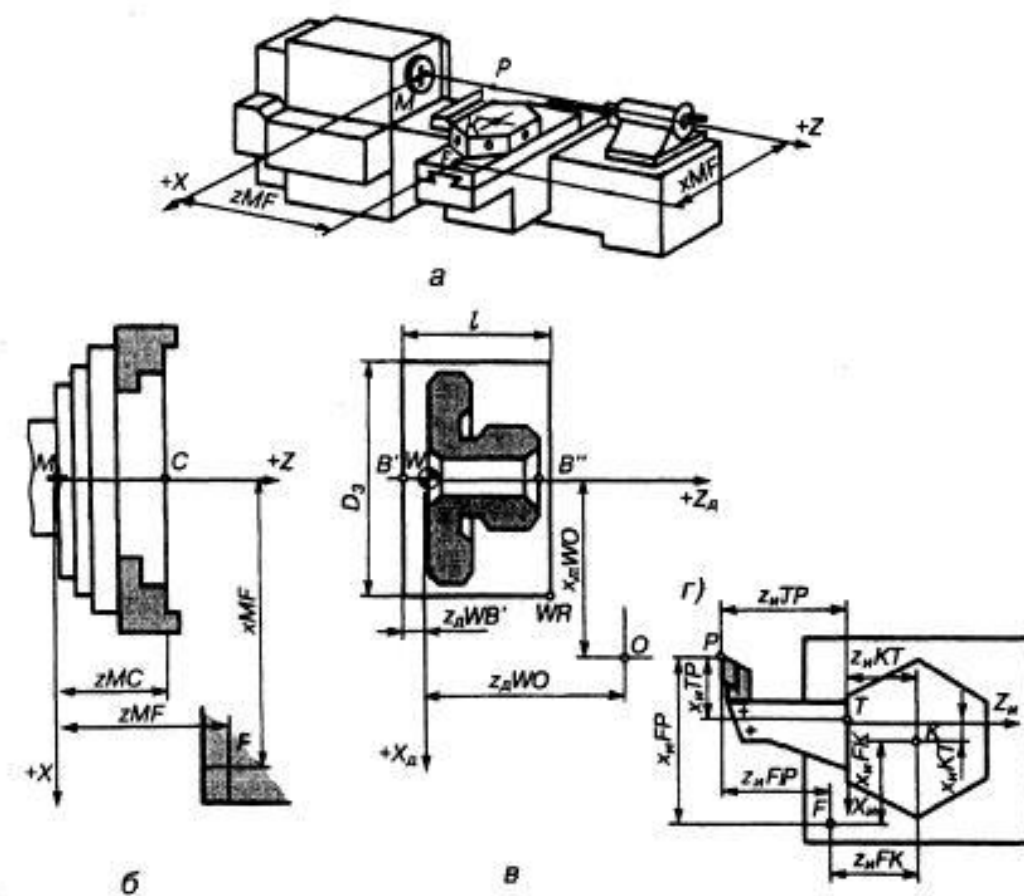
Система координат при обробці на токарному верстаті
